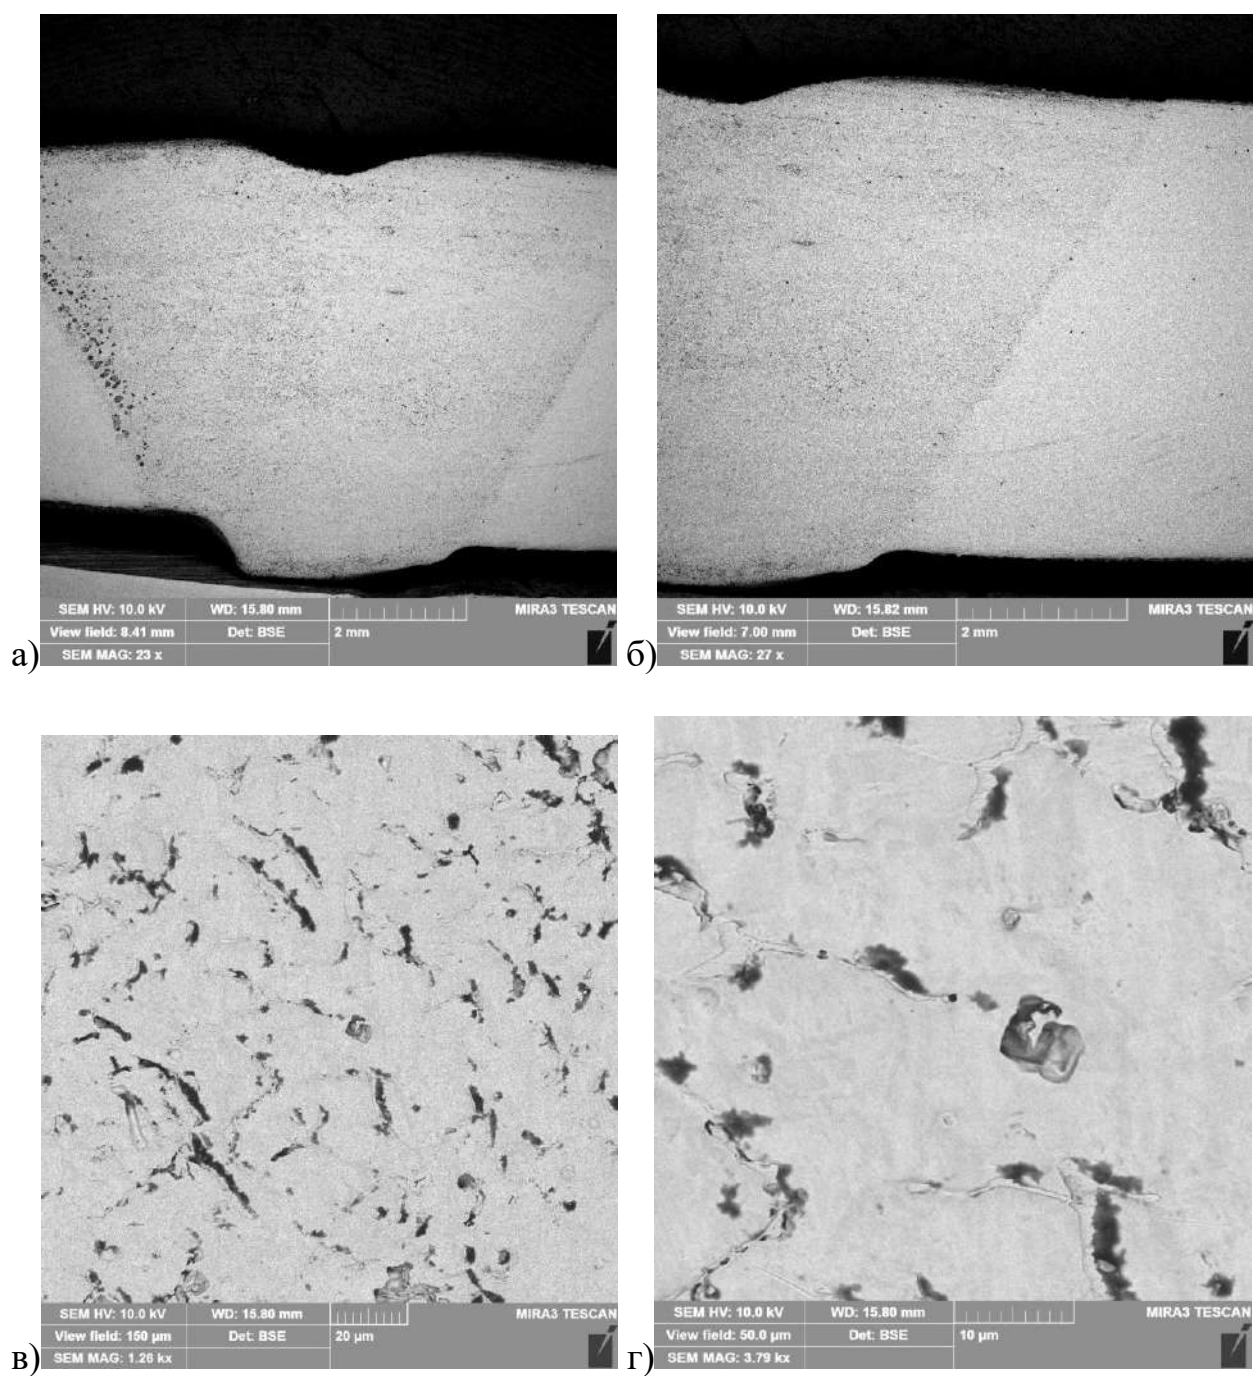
Мікроструктура металу зварного з'єднання (6 мм), що отримано плазмовим зварюванням: а, б – загальний вигляд зварного шва; в, г – метал шва при різних збільшеннях.
